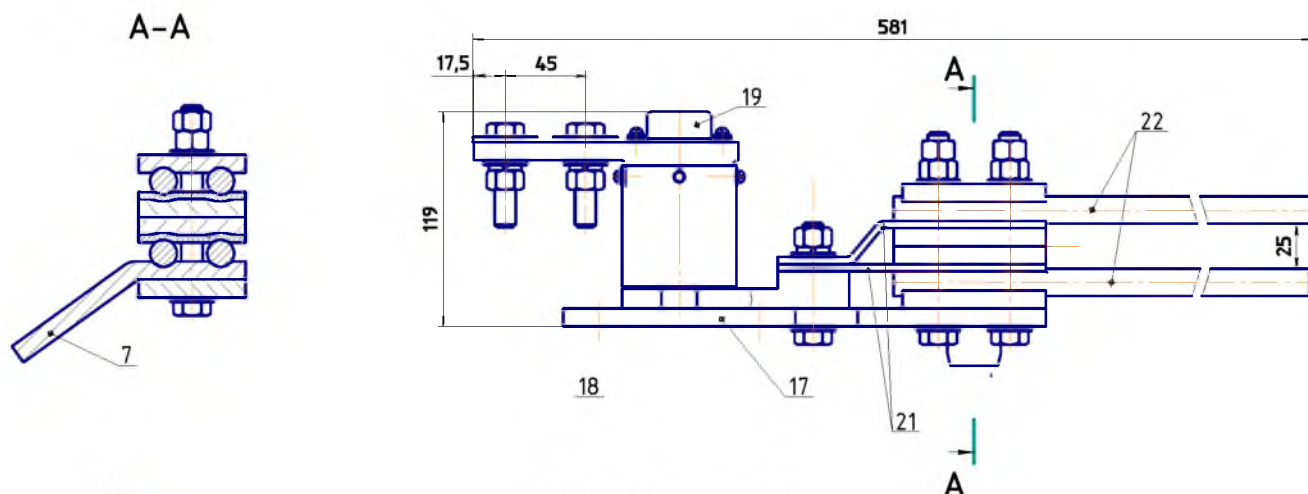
Разметка присоединительных отверстий на общей раме разъединителя
